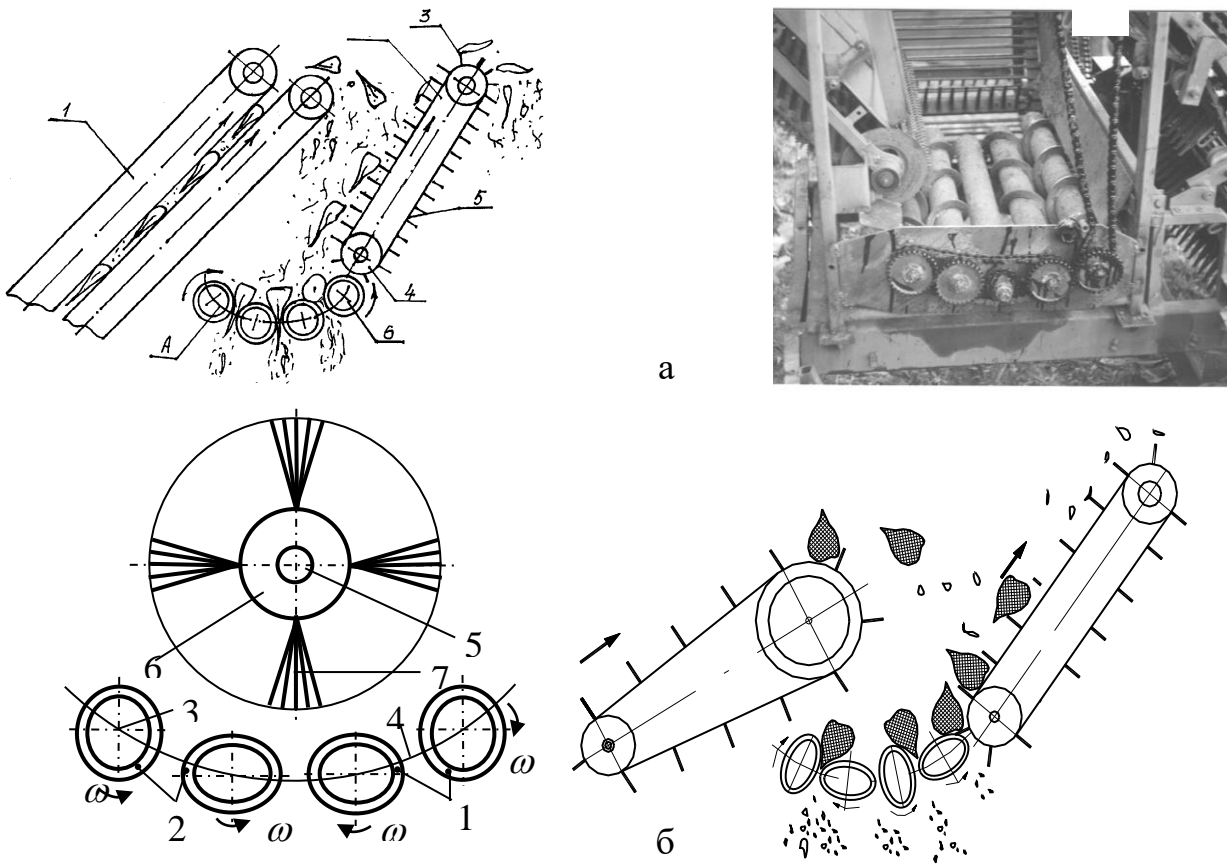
Схеми та загальний вигляд очисних систем: а – з шнеками круглого перерізу; 1 – транспортер; 2 – пальчикова гірка; 3, 4 – приводний і ведений вал; 5 – палець гірки; 6 – шнековий очисник; б – із еліптичними шнеками; 1, 2 – ліва та права системи еліптичних шнеків; 3 – вісь обертання; 4 – нижня вітка еліпса; 5 – очисний вал; 6 – барабан; 7 – очисні елементи.
